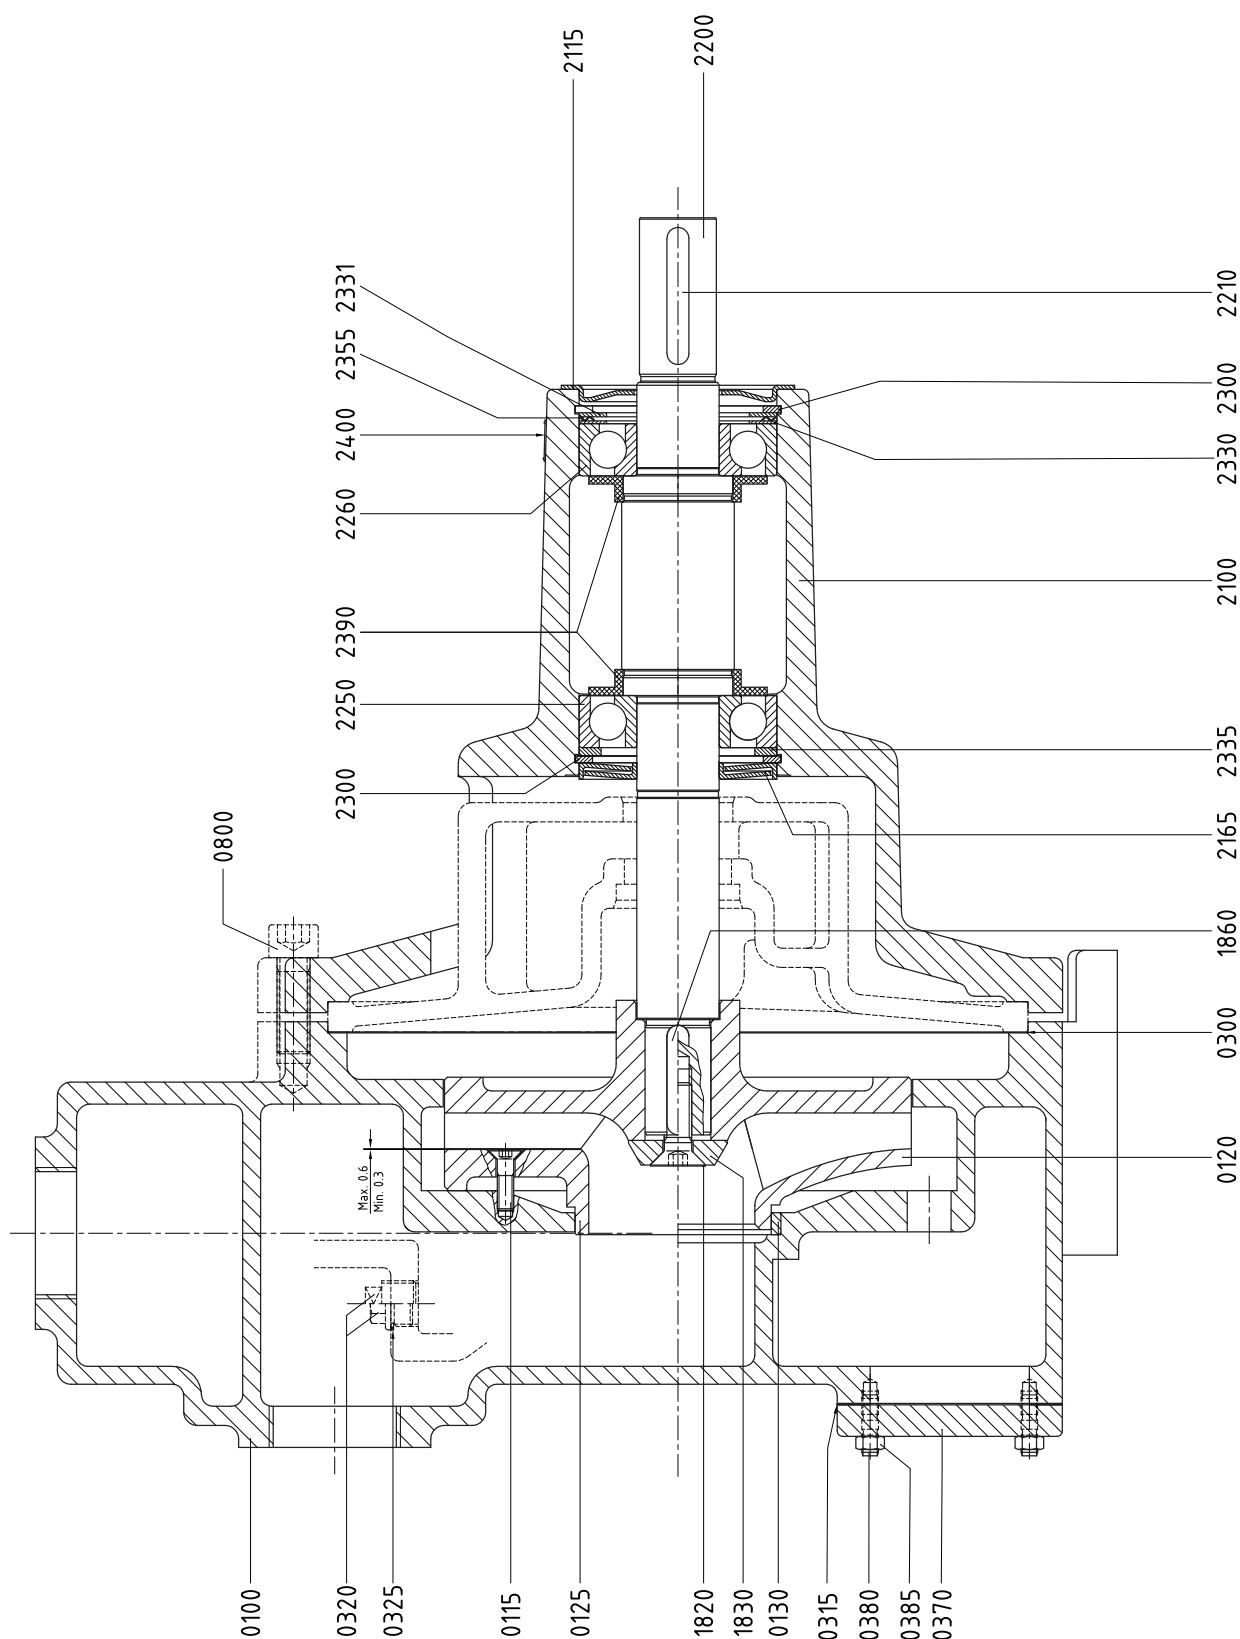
Чертеж в разрезе FRE - группа подшипника 3.
